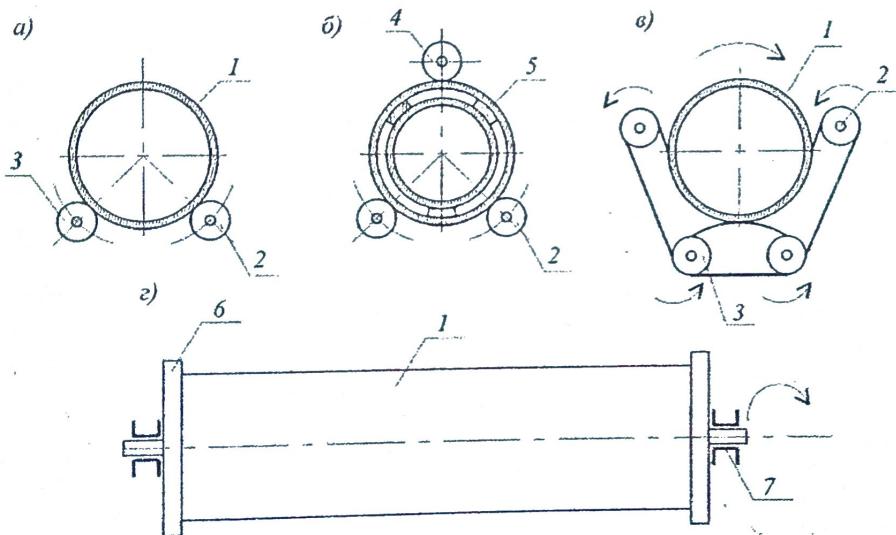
Типы центрифуг (СНиП II-21-75) а) - роликовая, б) - барабанная, в) - гиростатическая, г) - осевая; 1 - форма, 2 - опорный ролик, 3 - ролик, 4 - привод, 5 - барабан, 6 - планшайба, 7 - опорный подшипник, приводной
